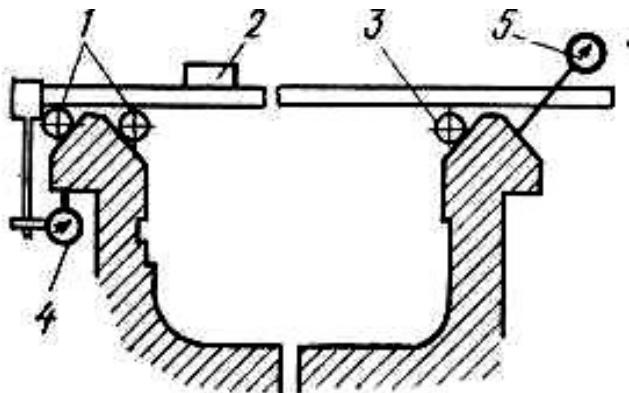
Схема универсального приспособления для проверки точности направляющих
